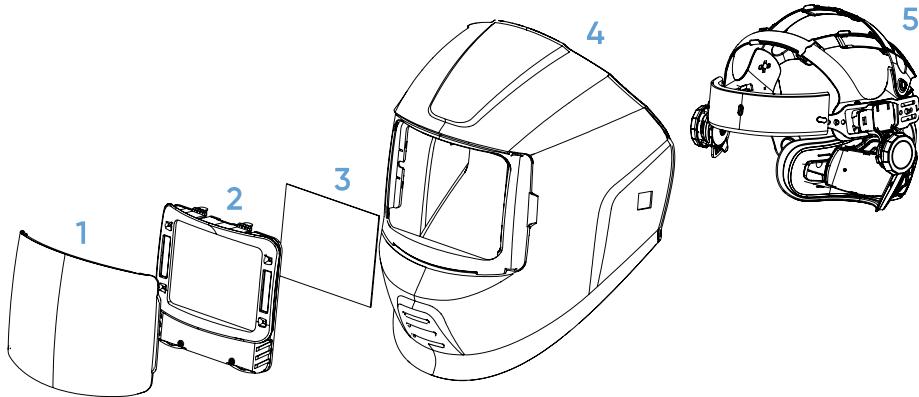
Внешний вид сварочной маски SHINE
